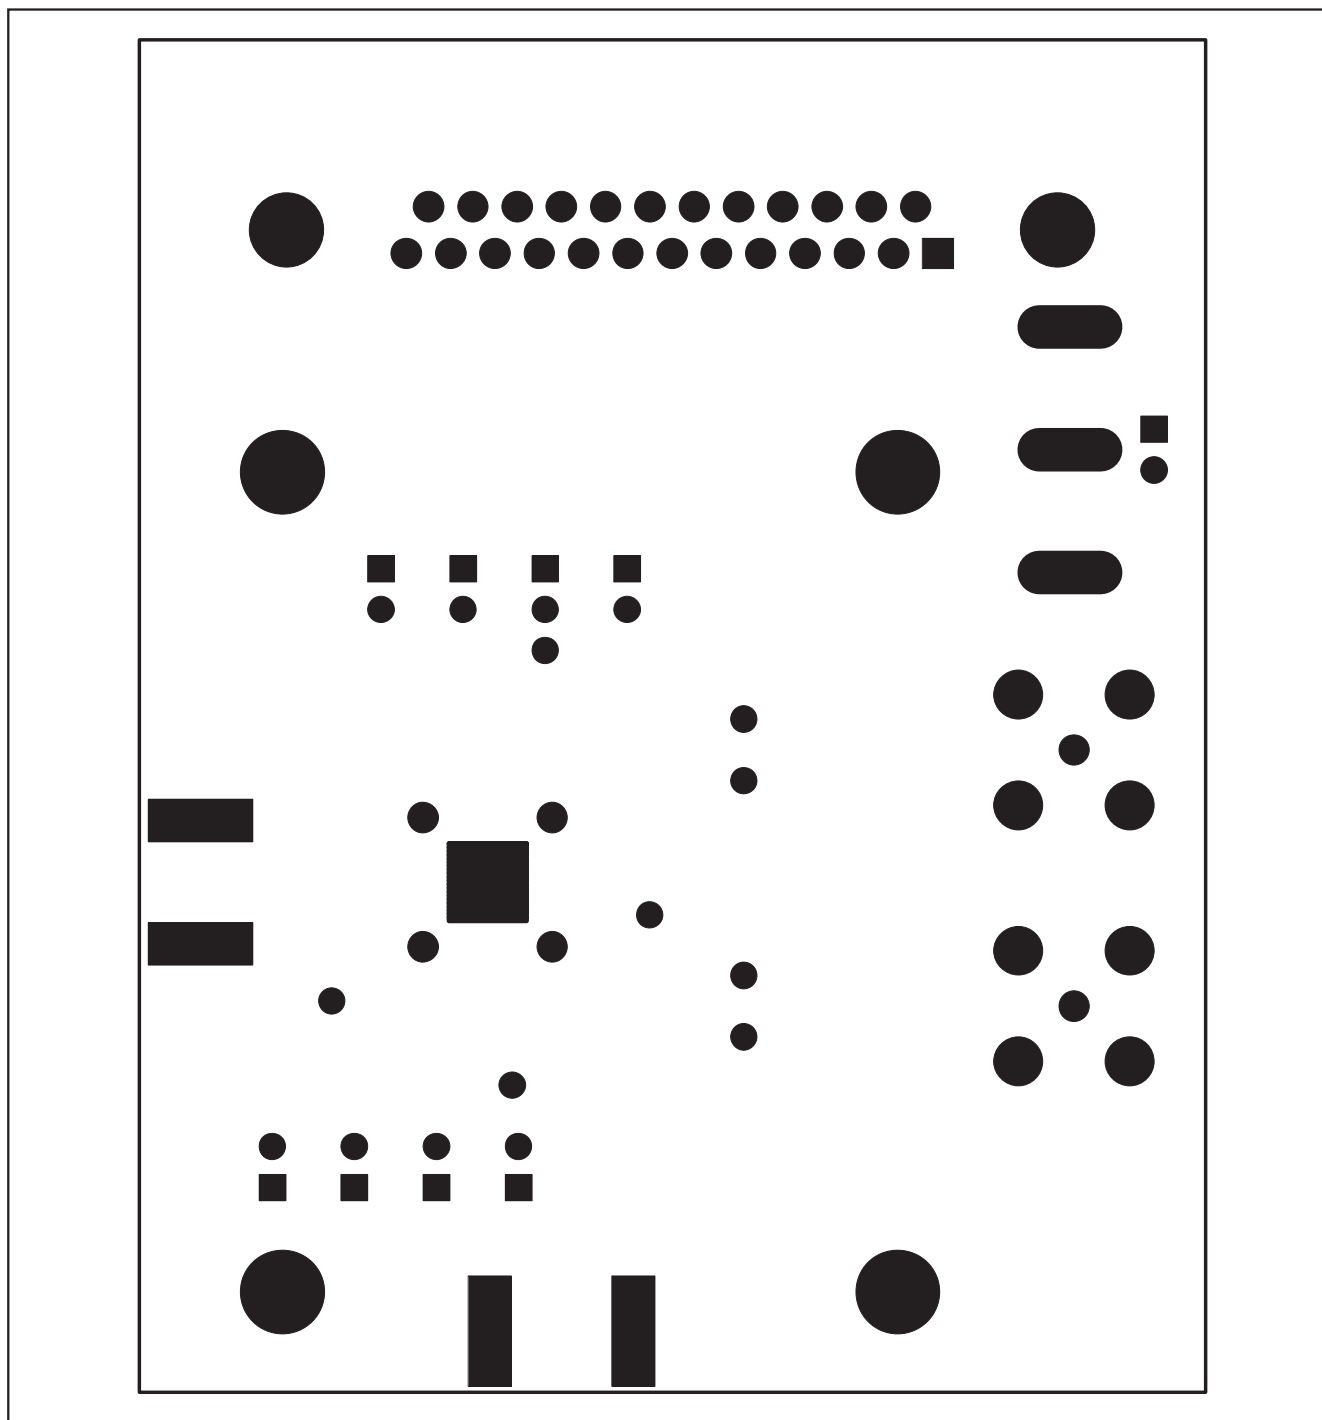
MAX2112评估板PCB布局—底层阻焊层
